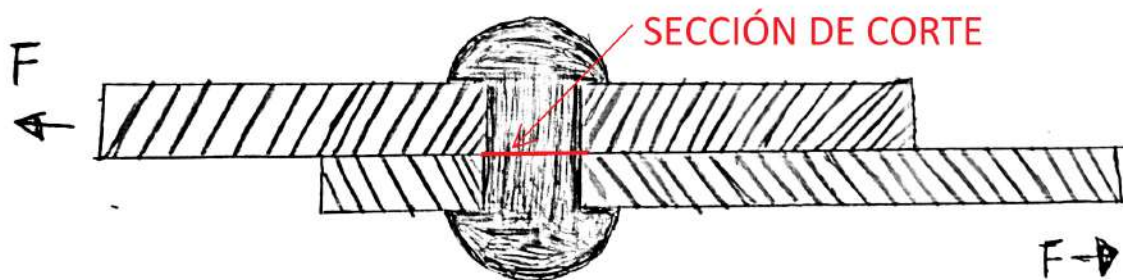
Esfuerzo de corte en un remache; Fuente: elaboración propia.
